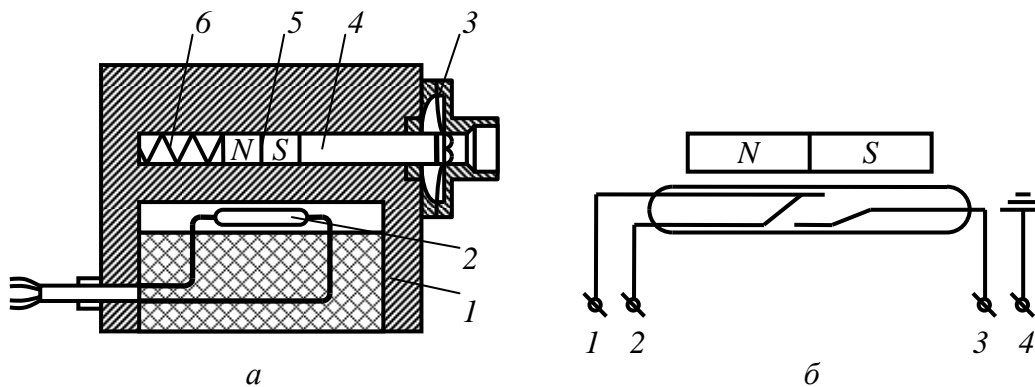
Перетворювач ПЕВ-1: а – конструкція; 1 – корпус; 2 – комутувальний елемент (геркон); 3 – мембрана; 4 – штовхач; 5 – постійний магніт; 6 – пружина; б – принципова схема; 1, 2, 3, 4 – контакти геркона
